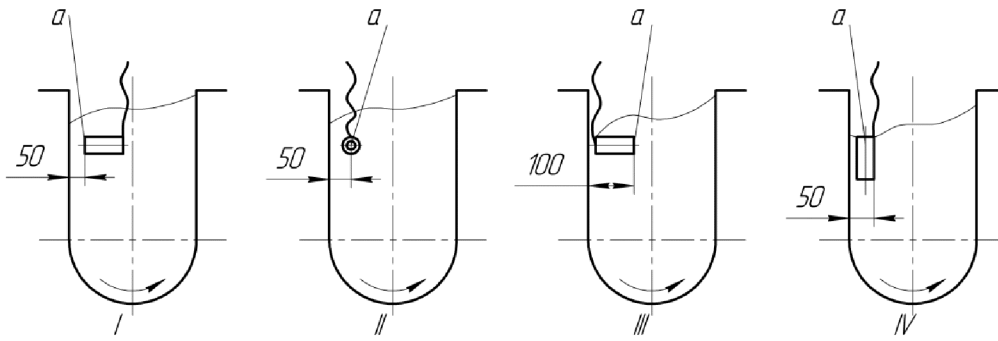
Схема расположения датчика-детали в резервуаре вибростанка:
